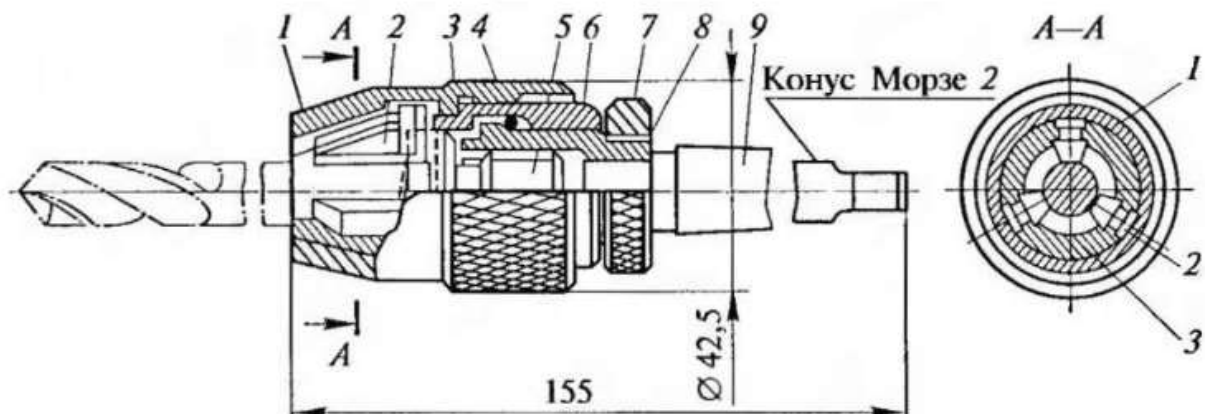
Трикулачковий безключовий свердлильний патрон
